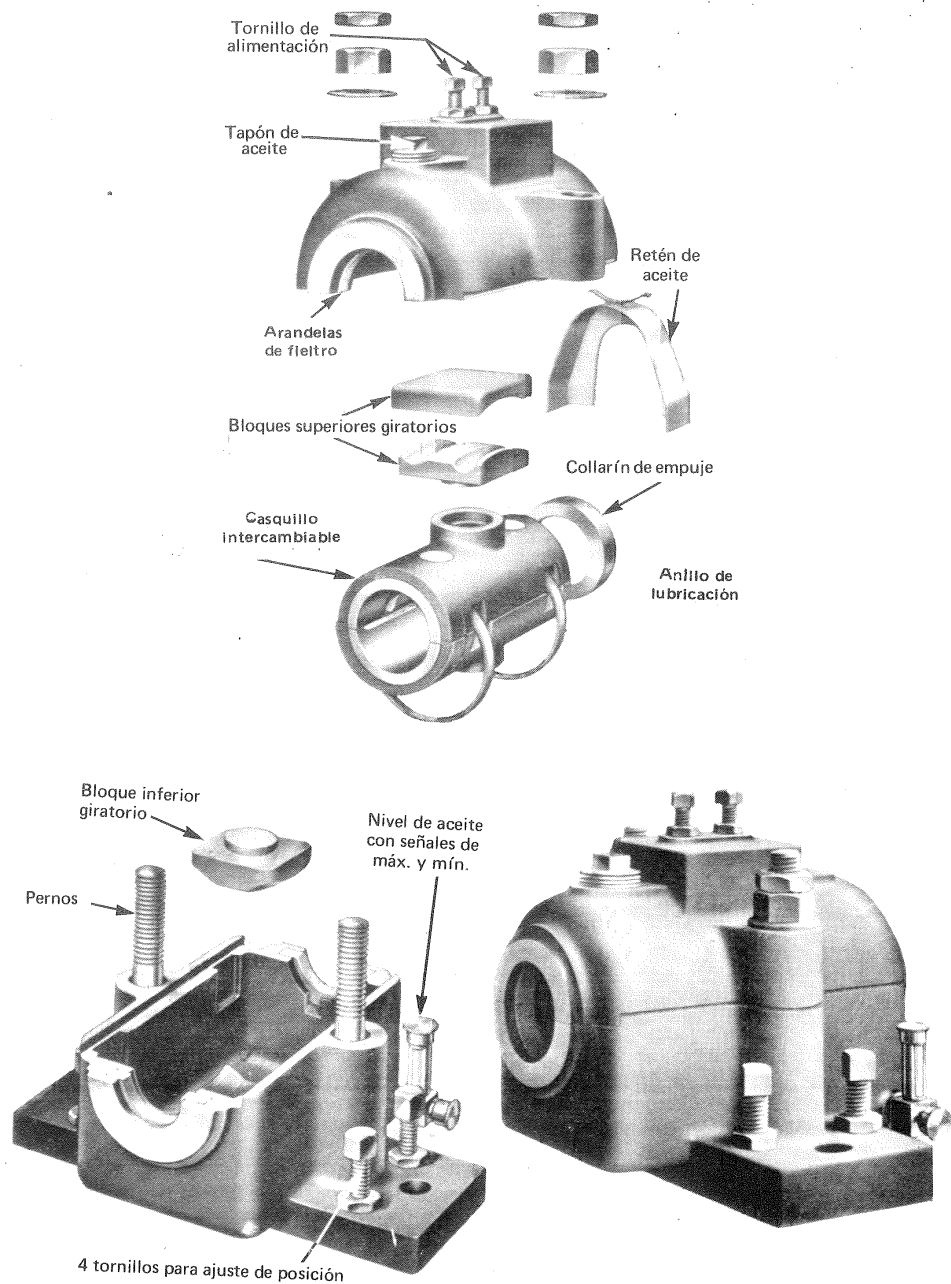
Cojinete de V: conjunto y despiece.
